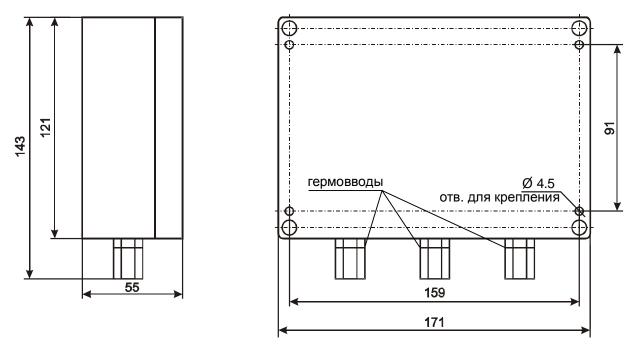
Внешний вид и габаритные размеры БРЛ в исп. IP65
